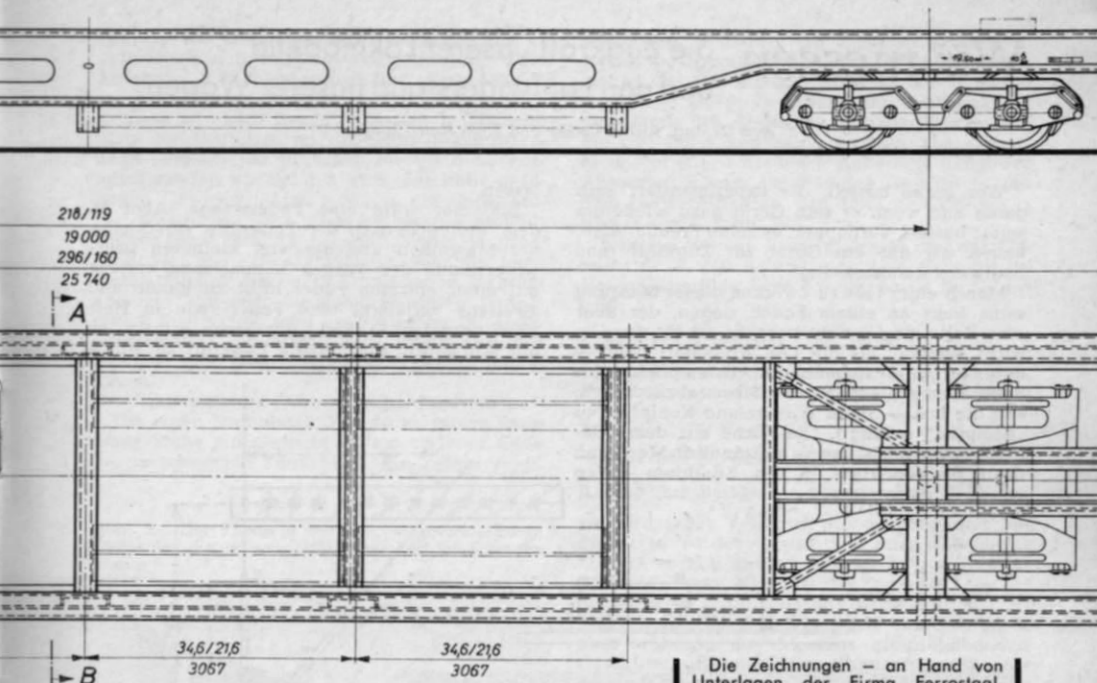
(ganz oben). Seitenansicht im Maßstab 1:87 (1:1 für H0). Die Maße vor dem Schrägstrich gelten für H0, die dahinter für N. Die Originalmaße sind unter der Maßlinie angegeben.
